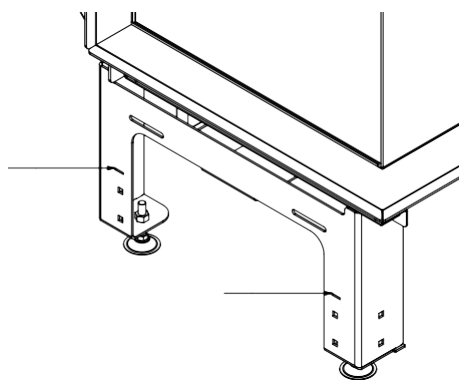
Перфоратор для разметки линии реза при установке нагревателя на стене.
